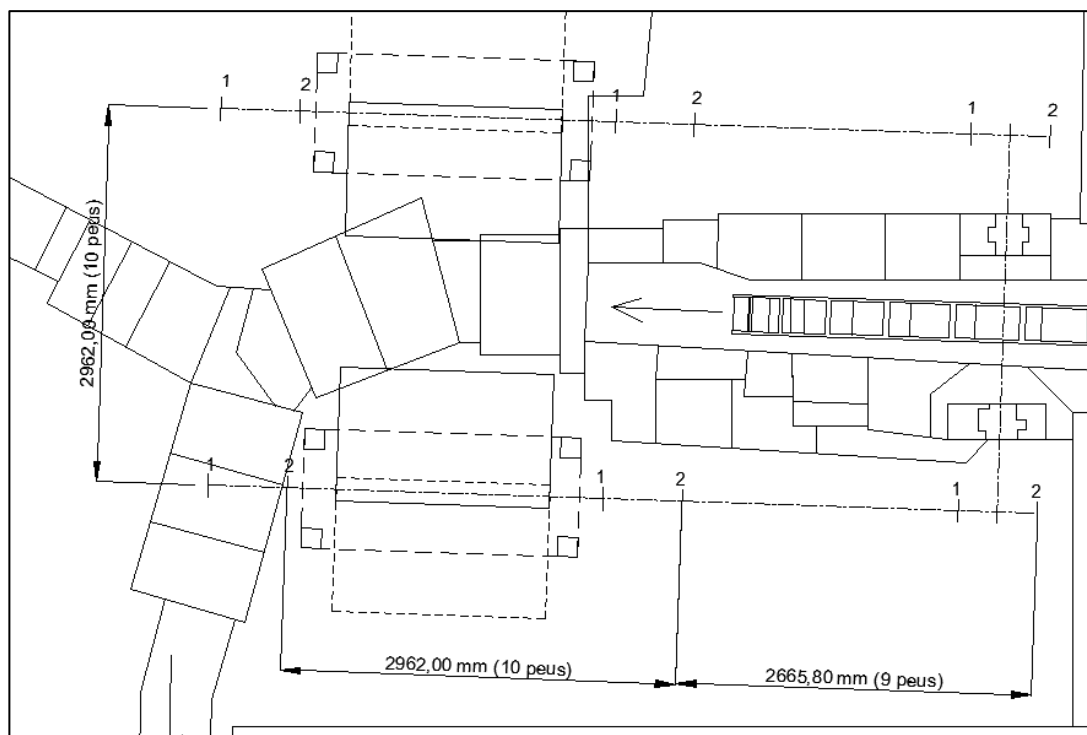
Vista en planta en les dimensions longitudinal de l'eix, de les bieles i de les serres
